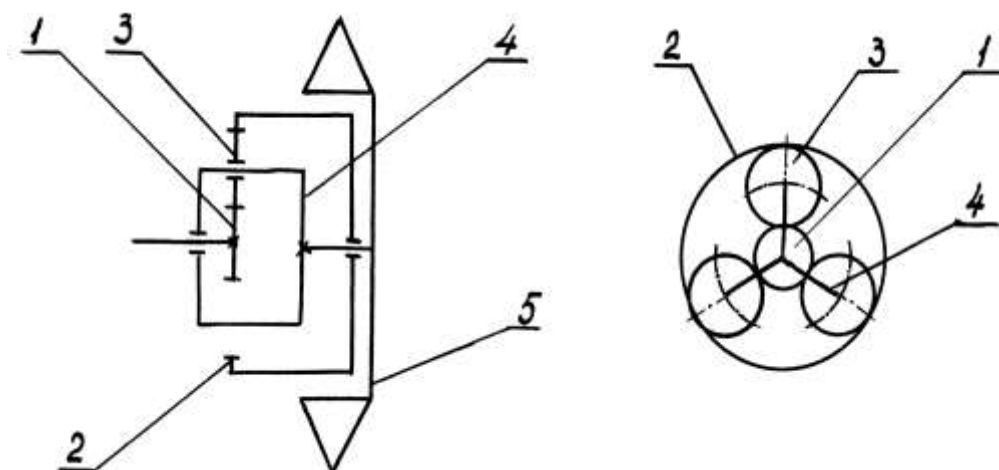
Схема соосного однорядного планетарного редуктора:
